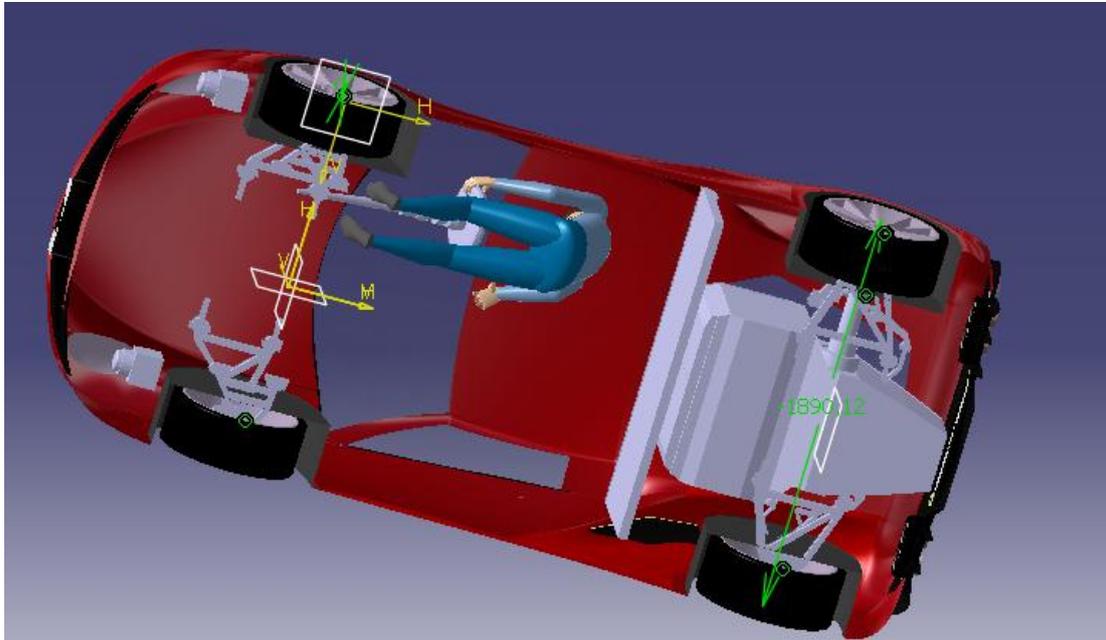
Layout meccanico 3D e oscar assemblati alla carrozzeria
